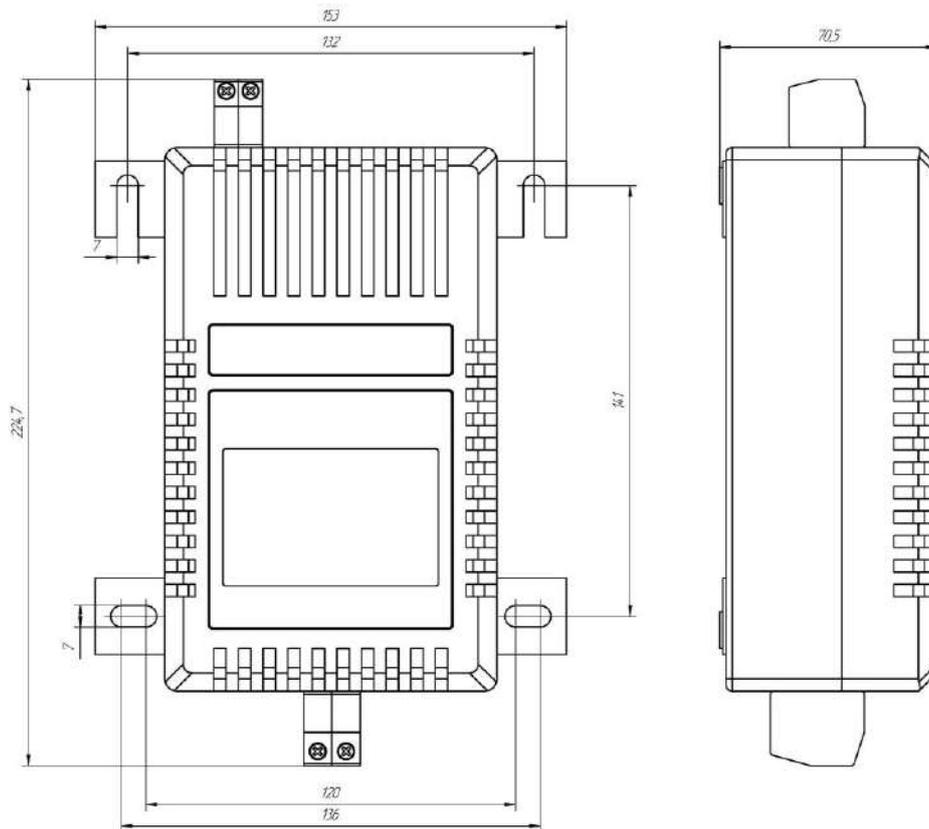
Габаритные и установочные размеры БУП
